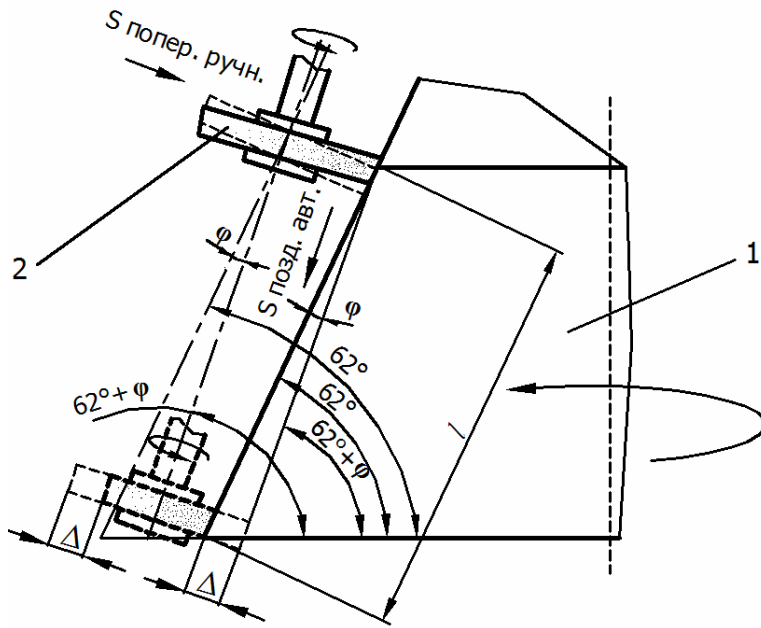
Розрахункова схема круглого шліфування з автоматичною поздовжньою і одночасно ручною поперечною подачами: 1– конус; 2 – круг.
